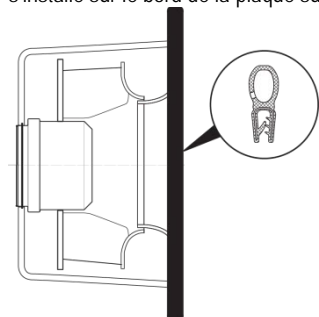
Vue latérale d'un RadiPac à structure à bras support et joint de bordure profilé côté entrée.
